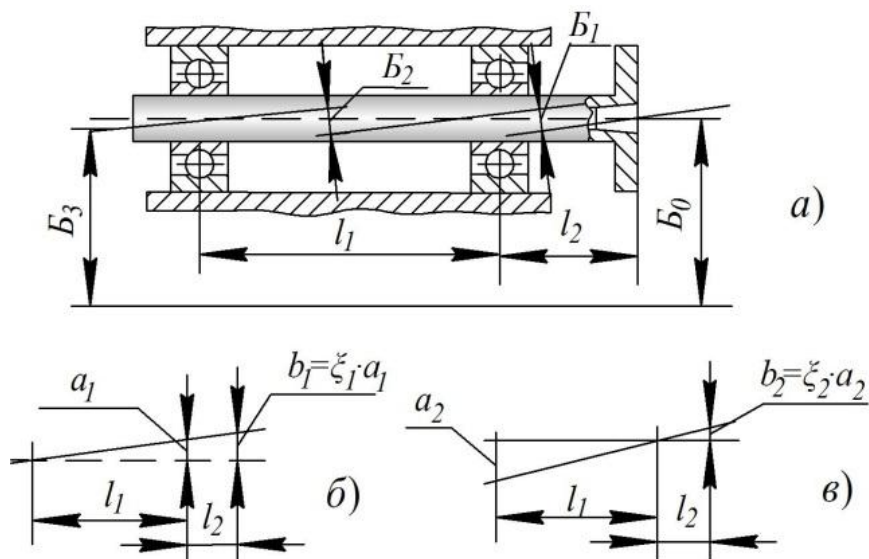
Вал, смонтированный в корпусе на двух подшипниках качения
